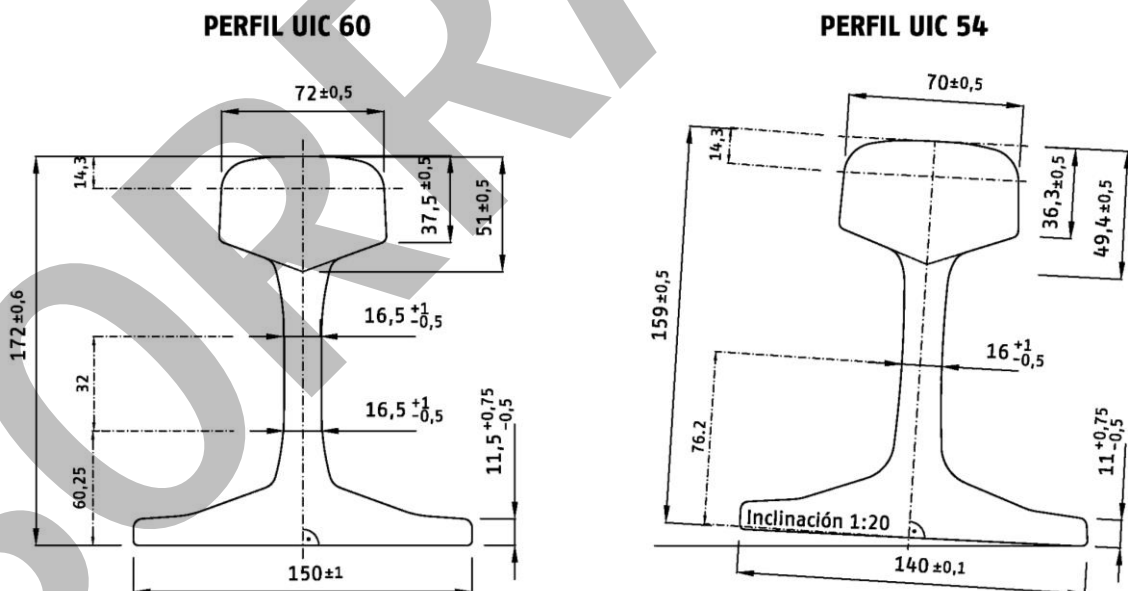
Dimensiones y Tolerancias del frente a soldar.
